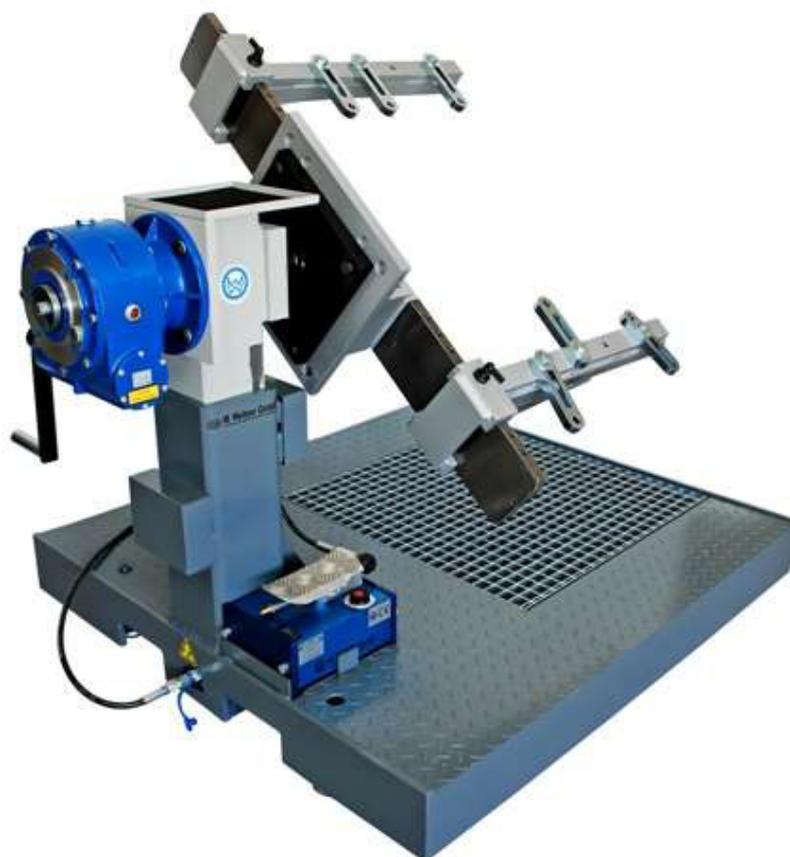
Стенд для переборки двигателей WW–HV–1500.
